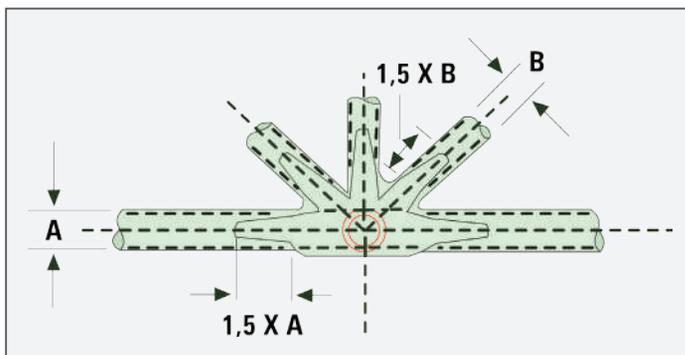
Posicionamento e dimensões do reparo em estrutura tubular
